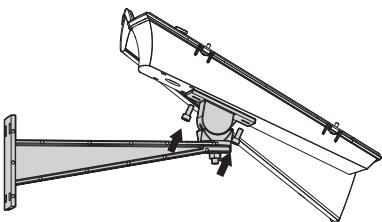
Befestigung auf der Halterung mit externer Kabelführung
